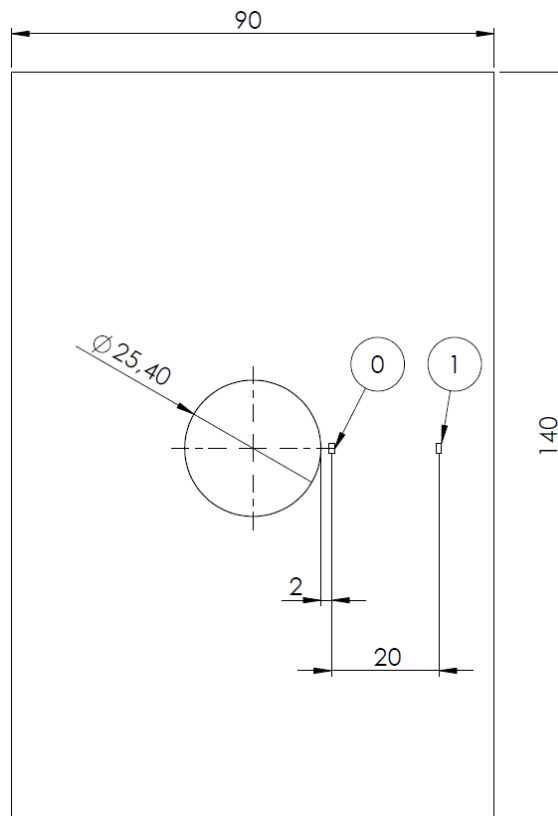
Desenho esquemático da placa de material isotrópico utilizada, em milímetros.
